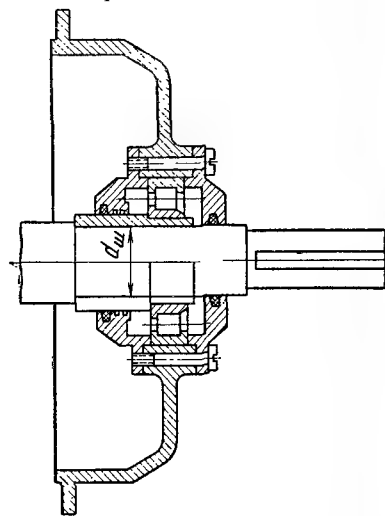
Вариант перевода электродвигателя с подшипников скольжения на подшипники качения.
